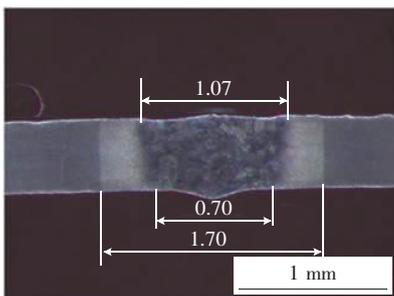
800 W,3 m/min的焊缝宏观形貌
